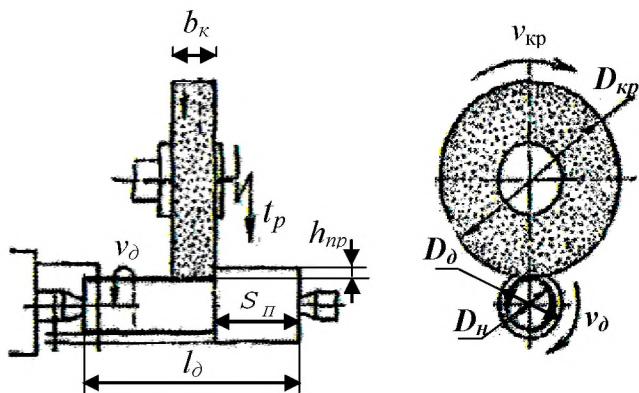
Схема обробки шліфувальним кругом деталей класу "вали":
